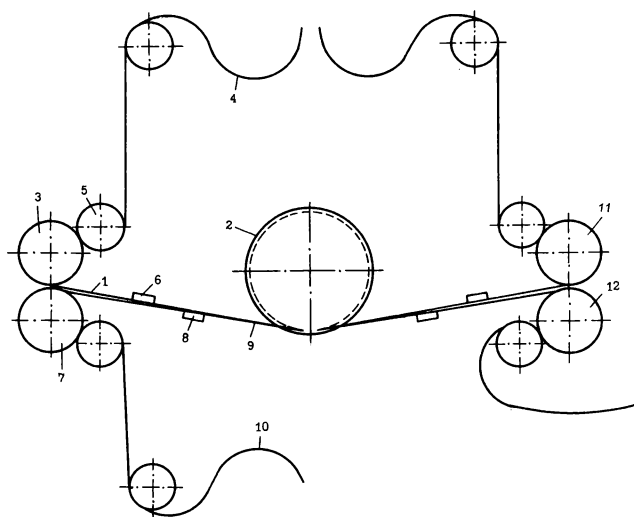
Схема печатной головки с устройствами для создания натяжений
